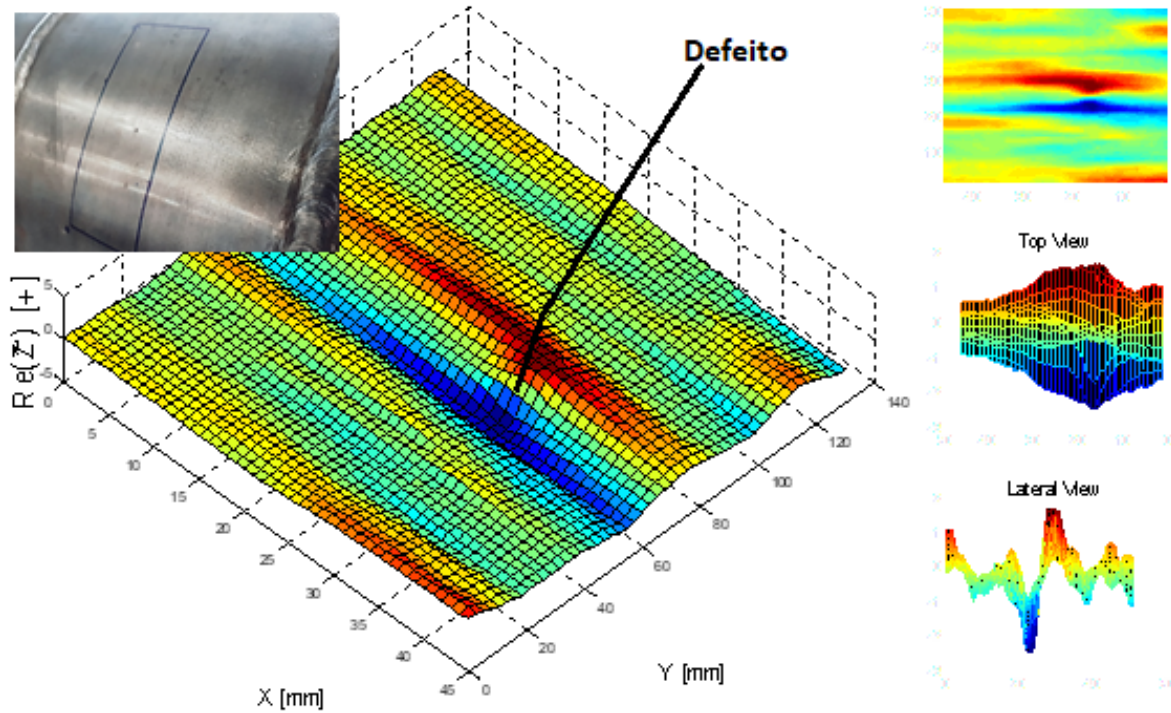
Scanned surface do tubo com o defeito circular padrão.
